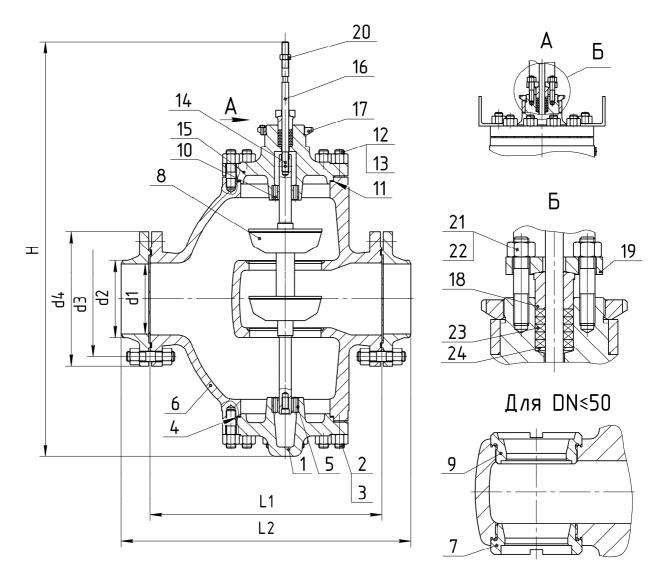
Габаритные размеры клапана СКБК2, сальниковая набивка из материала "Графлекс"
